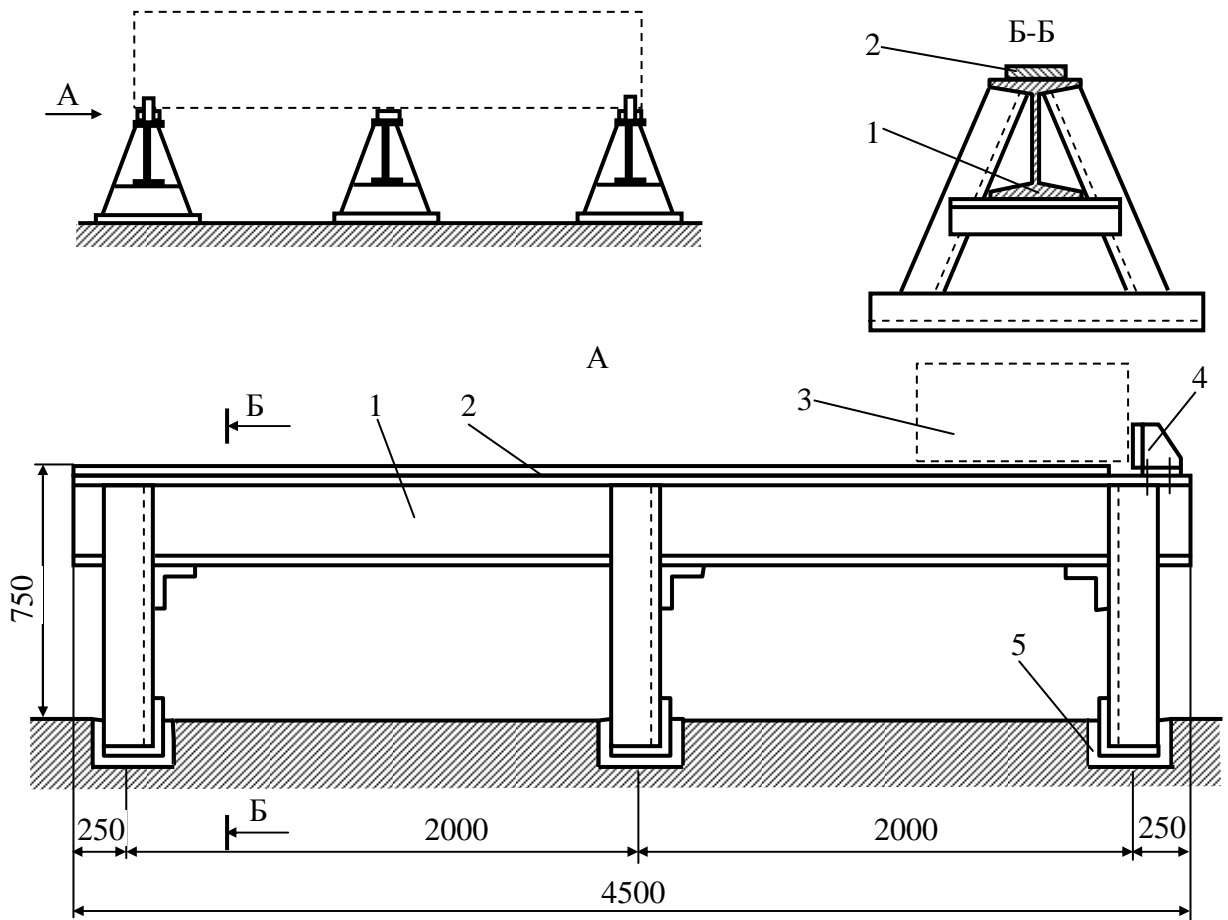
Пересувний стелаж: 1-опорна балка; 2-штаба; 3-виріб; 4-упор; 5-напрямна.
